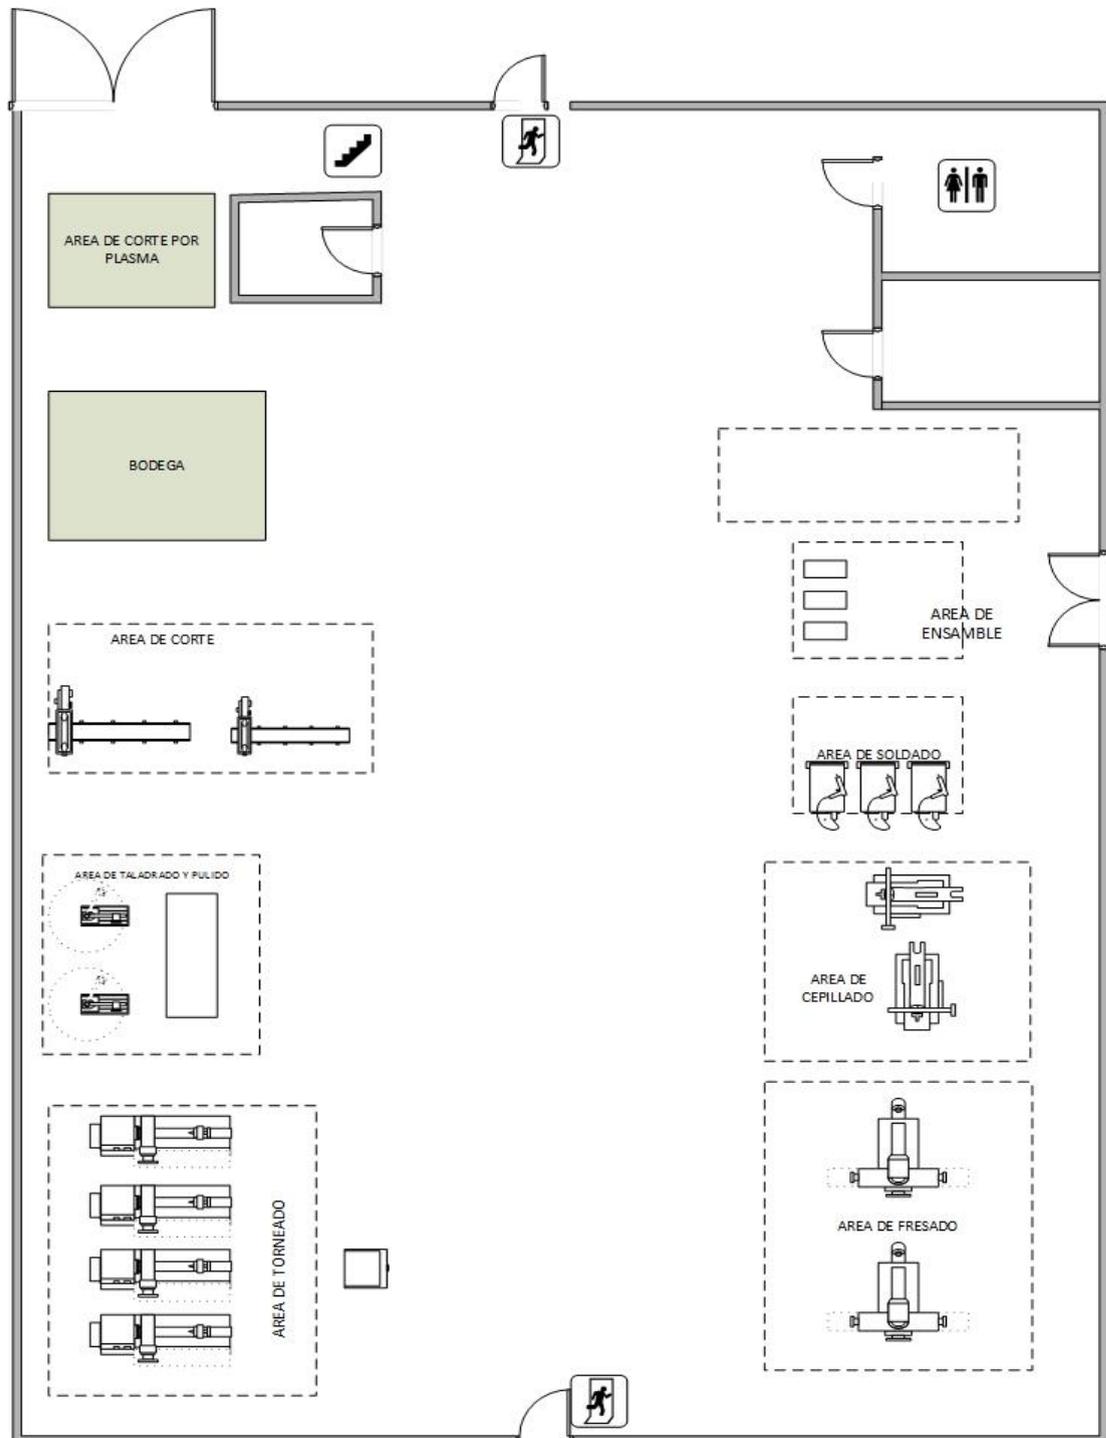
Layout de la planta de producción de Maquinarias Espín.
